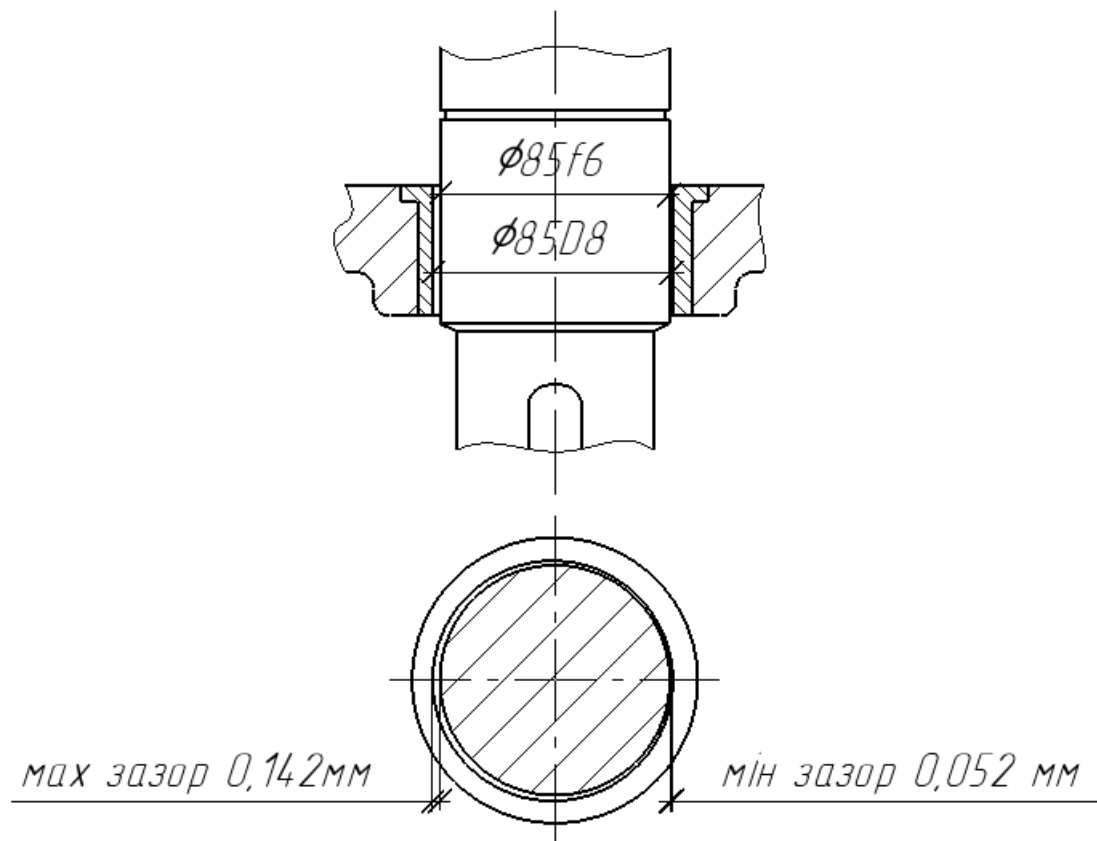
Люфт бронзової вкладки корпуса підшипника
